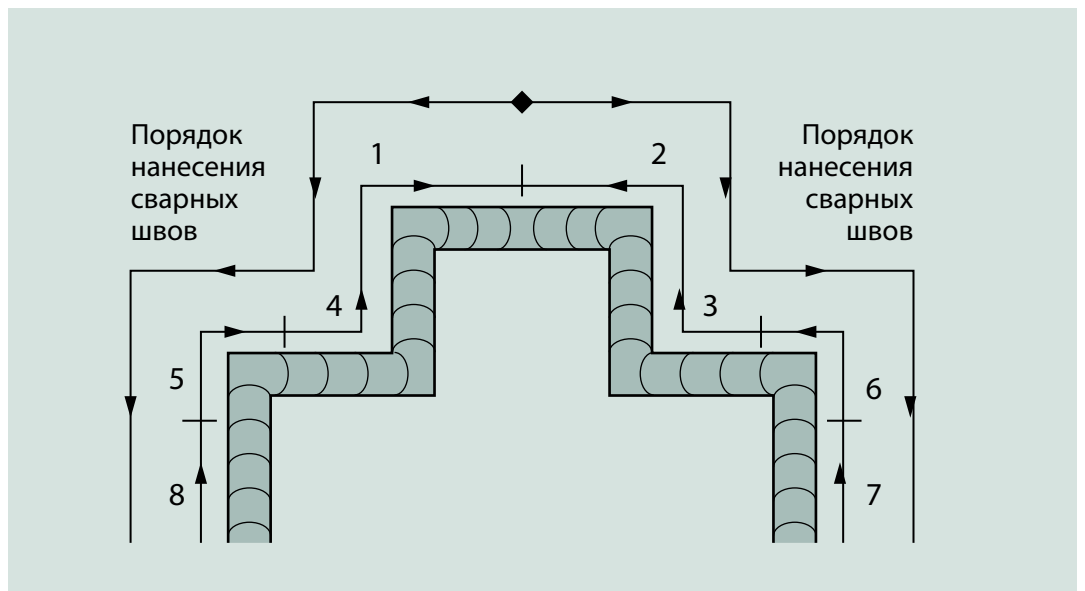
Образец технологии обратноступенчатой сварки
